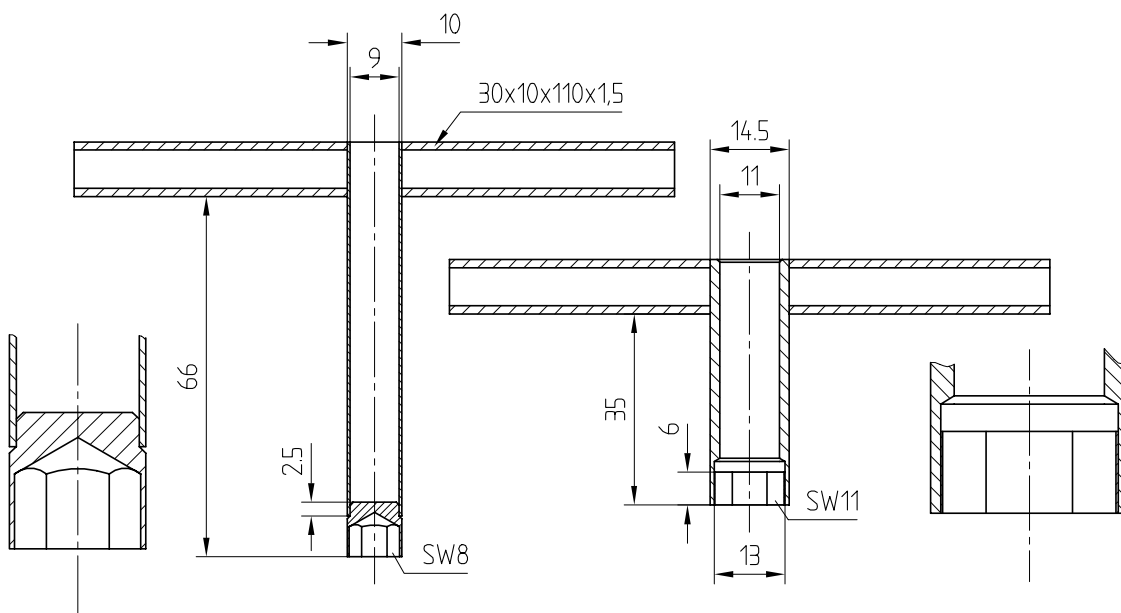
Einstellwerkzeug für Shimano Pedale
